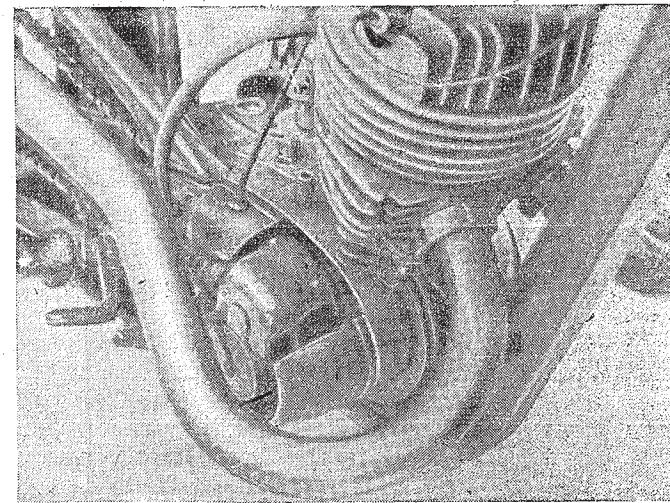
Общий вид установки магнето M27-Б на двигателе ИЖ-49
